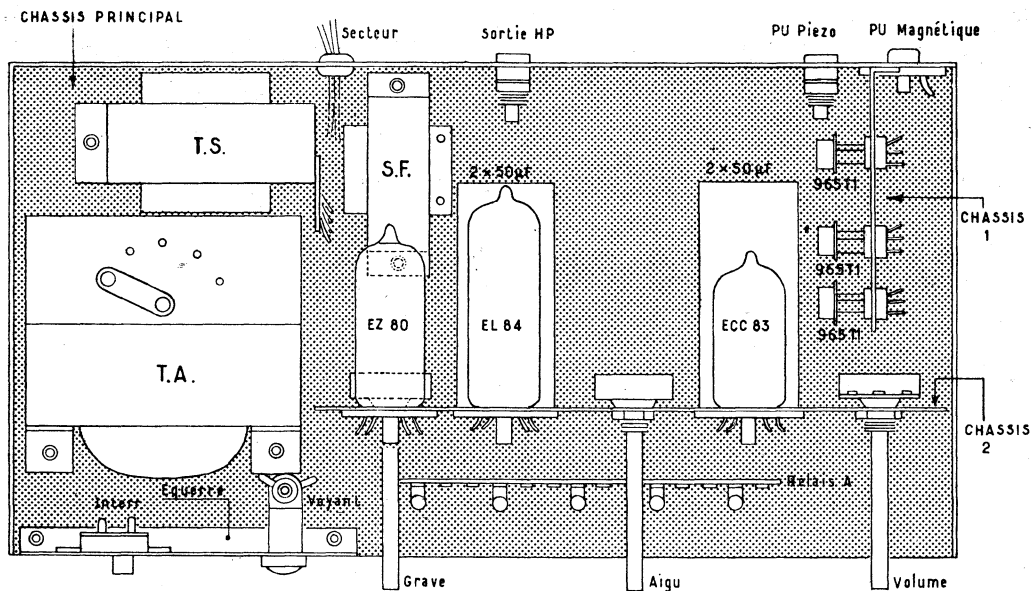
ASSEMBLAGE DES CHASSIS - DISPOSITION DES ELEMENTS
